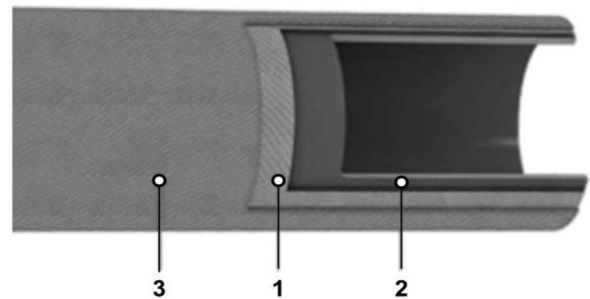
Конструкция напорного рукава с армирующим каркасом из нитей натуральных волокон. 1 – наружный защитный слой; 2 – внутренний гидроизоляционный слой; 3 – армирующий каркас
